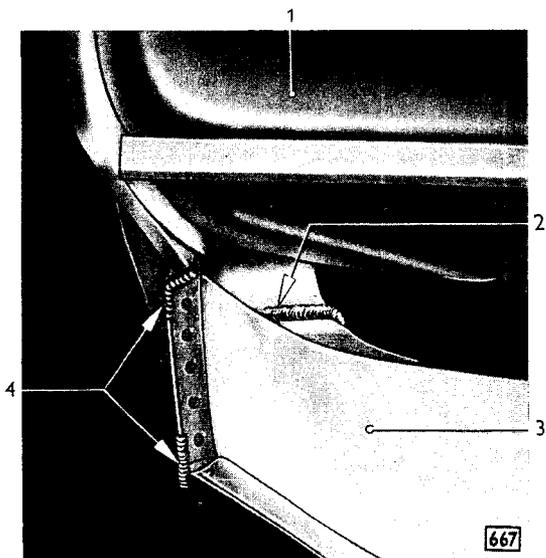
Oberseite der rechten Seitenstrebe an Seitenstrebenrest lichtbogengeschweißt- Linke Seitenstrebe in gleicher Weise lichtbogenschweißen
